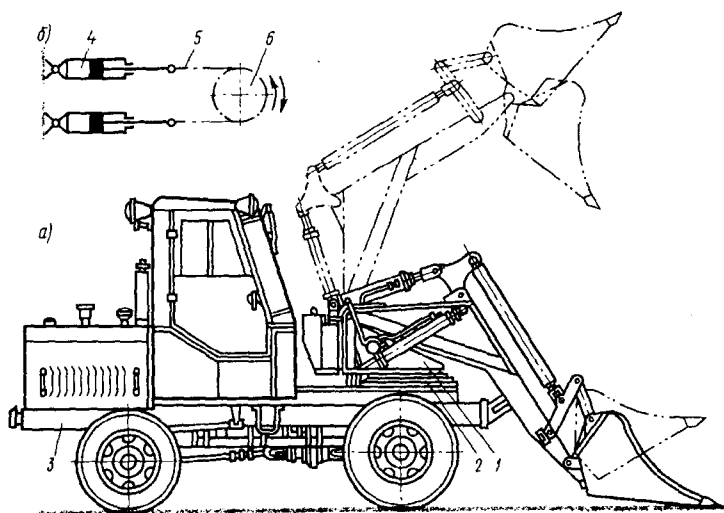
Полуповоротный одноковшовый погрузчик: а – схема конструкции; б – кинематическая схема механизма вращения платформы.
